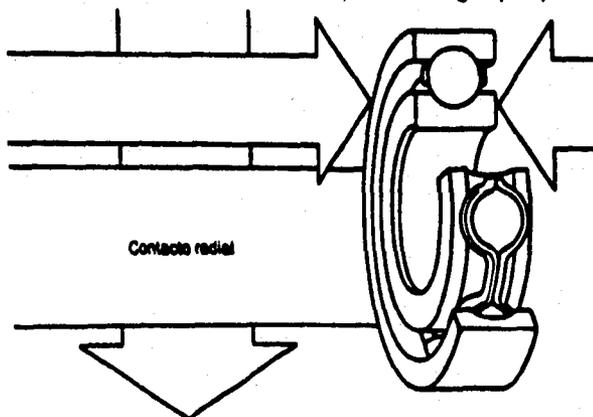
Rodamiento de bolas de una hilera y ranura profunda.
